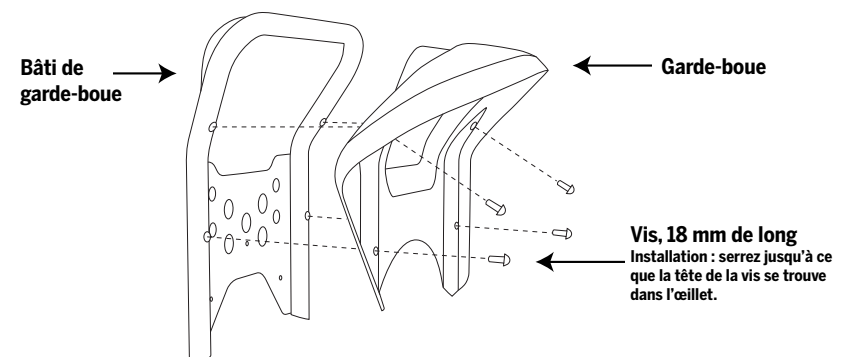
Retrait ou installation du garde-boue et du cadre du garde-boue
